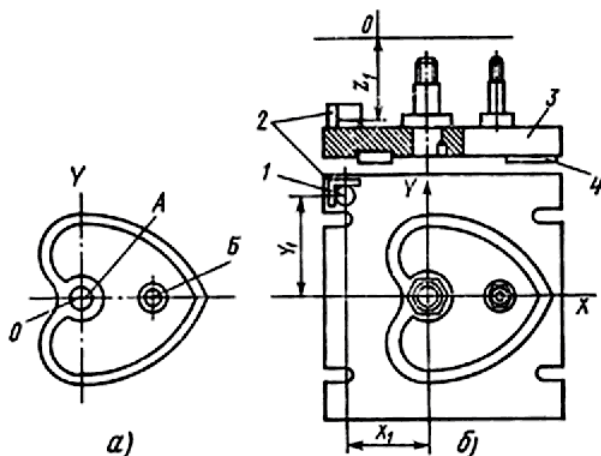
Обрабатываемая деталь (а) и установочное приспособление (б)
